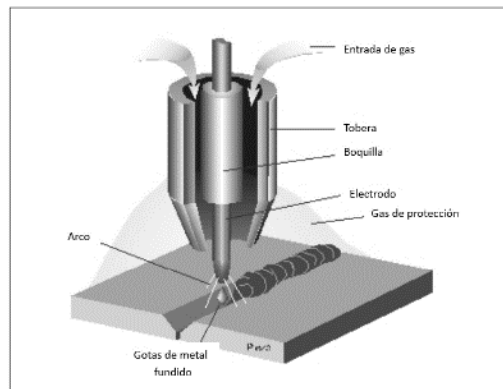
Esquema proceso de soldado MIG (Indura, pag. 82)
